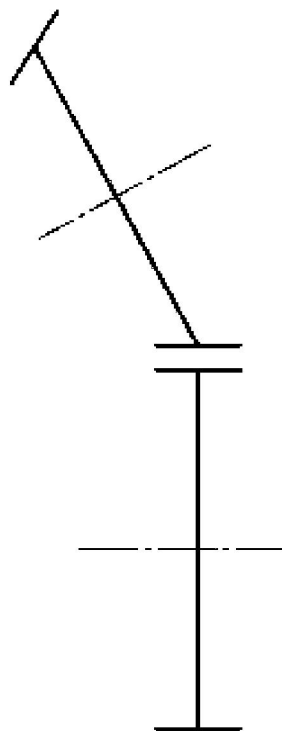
Кинематическая схема цилиндриконической передачи с пересекающимися осями внешнего зацепления
